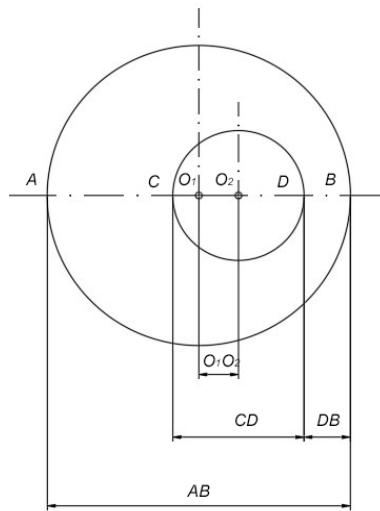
Эскиз приводного вала и эксцентриковой втулки
